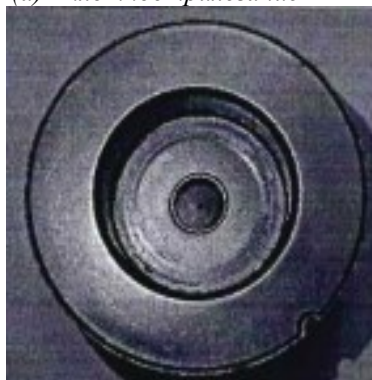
Ведущая шестерня рулевого механизма и расположение пятна контакта
